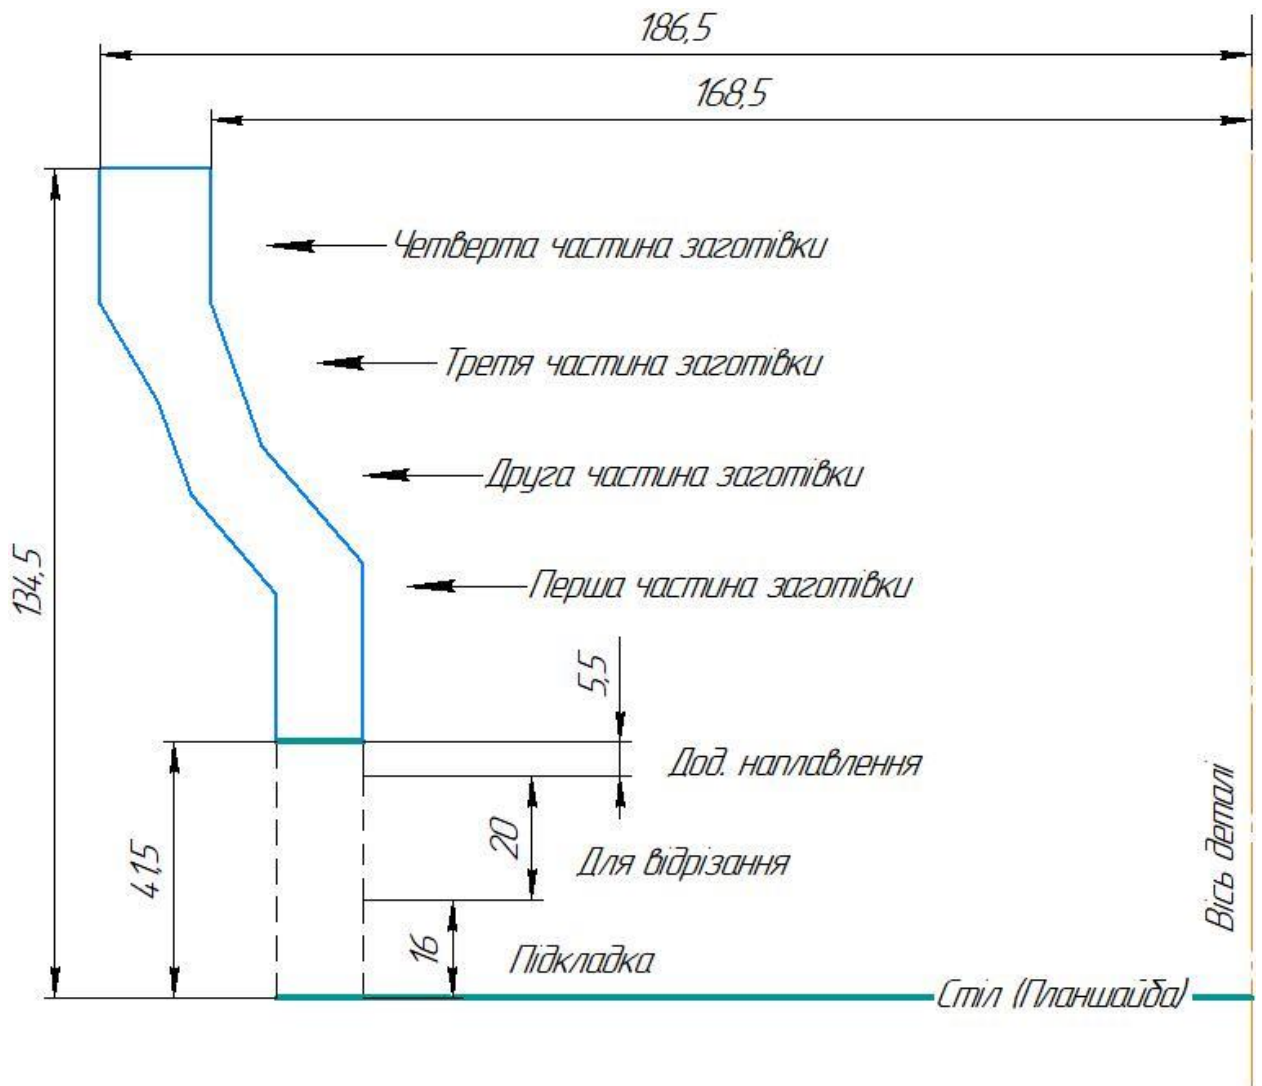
Креслення четвертої частини заготівлі 4500301001 (Зроблено в КОМПАС-3D v17)
